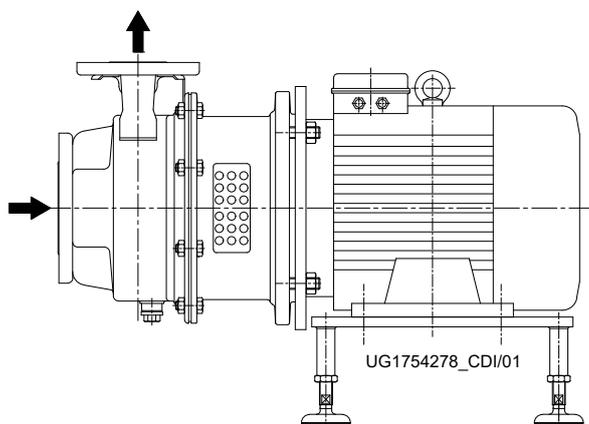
Tornillo de nivelación, desde el tamaño de motor 80 = 0,55 kW hasta 225 = 45 kW
